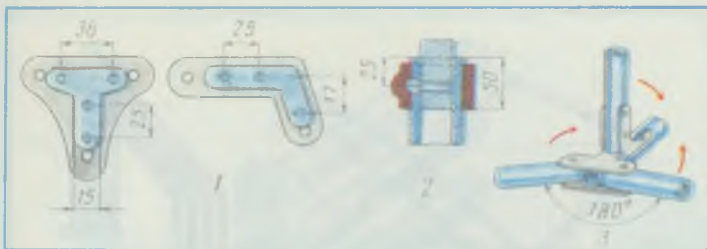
Крепежные детали: 1 — подгонка шарнирок; 2 — шариковый стопор; 3 — крепление вертикальной задней стойки.
